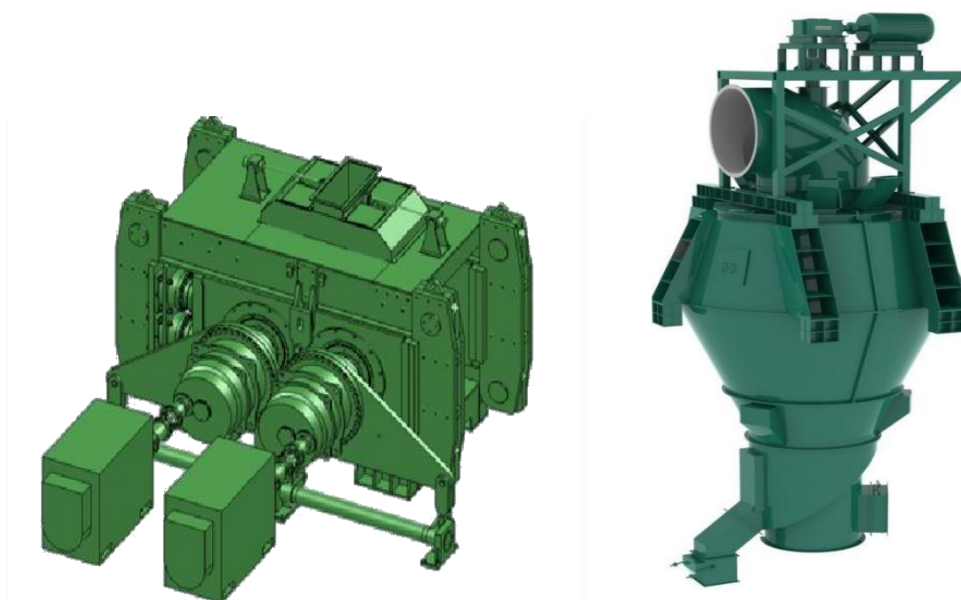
Внешний вид роликового пресса и динамического порошкового сепаратора
